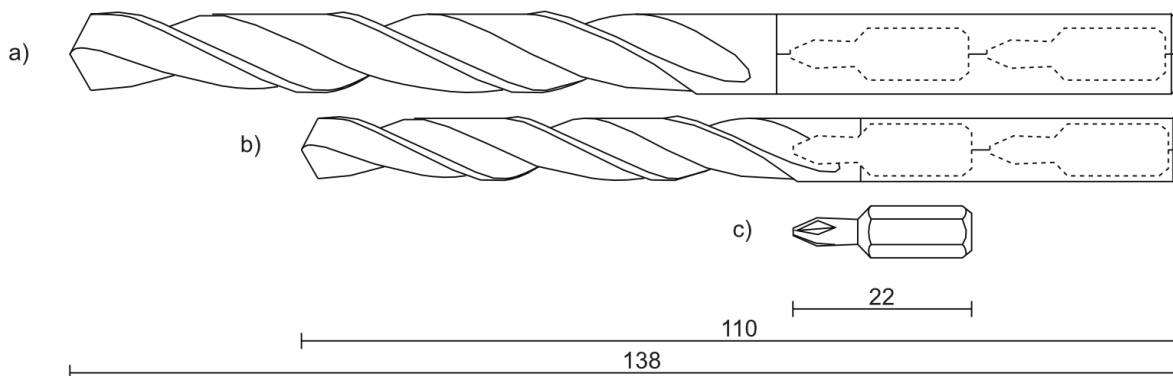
Spiralbohrer a) mit 10 Millimeter Durchmesser und Spiralbohrer b) mit 8 Millimeter Durchmesser eignen sich theoretisch zur Aufnahme von bis zu zwei Bits c) mit einer typischen Sechskantaufnahme in ¼ Zoll. Eigene Darstellung.
